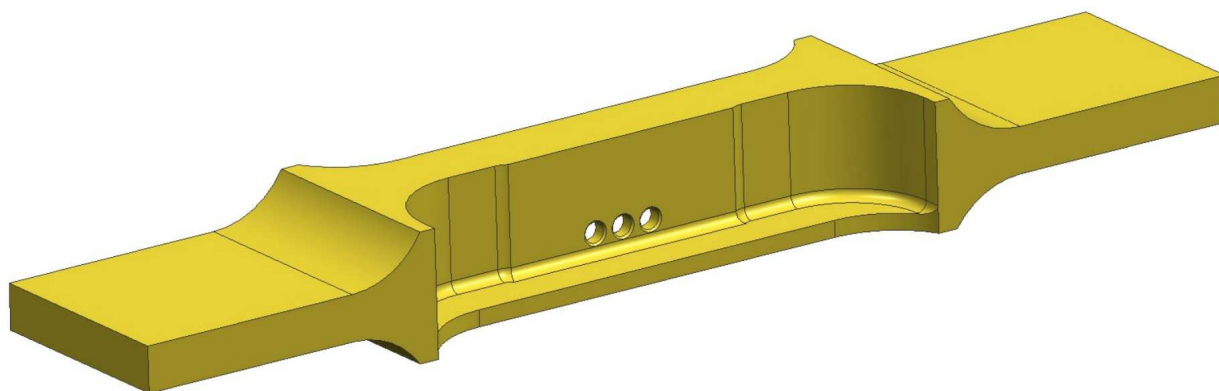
Трехмерная модель конструктивно-подобного образца стрингера для проведения усталостных испытаний
